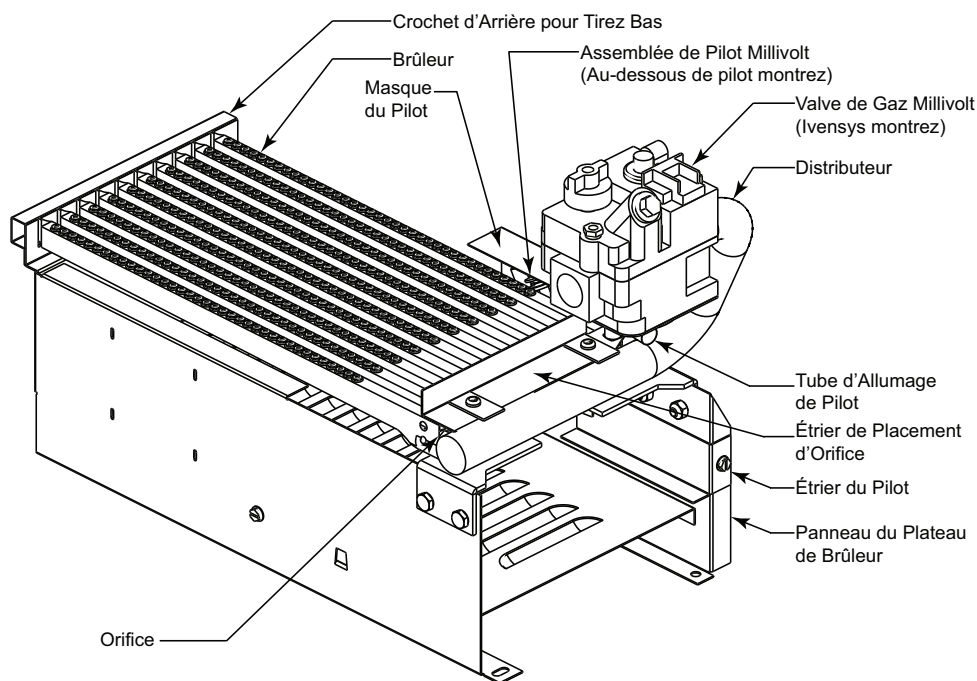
Millivolt Assemblée du Plateau du Brûleur
